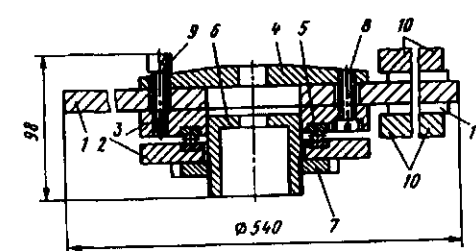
Сепараторная наладка эксцентрикового механизма двухдискового станка для доводки цилиндрических поверхностей: 1 – IV – элементы базирования в сепараторах; 1 – сепаратор; 2, 3 – диски; 4 – пластина; 5 – подшипник; 6 – втулка; 7 – гайка; 8 – винт; 9 – фиксатор; 10 – притиры; 11 – деталь
